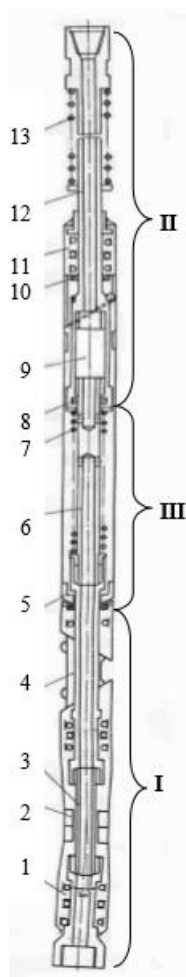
Отклонитель «КЕДР»: 2 - корпус с жёстким сменным искривленным патрубком, в подшипниковых узлах 1 которого размещен роторный вал 3; 4 - выдвижной клиновидный ползун; 5 - наружный шарнир; 6 – роторный вал; 7 - возвратная пружина, 8 - разделительное кольцо, 9 - втулка с шлицами; 10 - узел блокировки верхнего роторного вала 12 с пружиной 11; 13 – пружина
